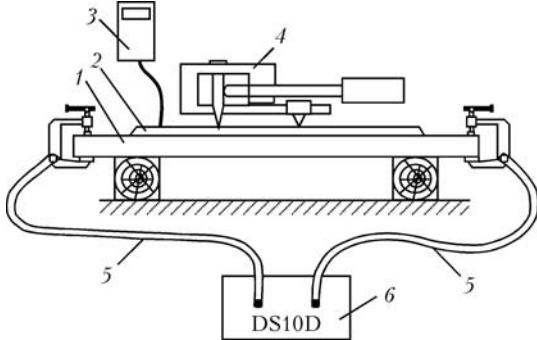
Схема проведения ЭФО с изучением характера деформирования образца: 1 — обрабатываемый образец; 2 — шов; 3 — мультиметр; 4 — деформометр; 5 — кабели; 6 — установка для ЭФО
